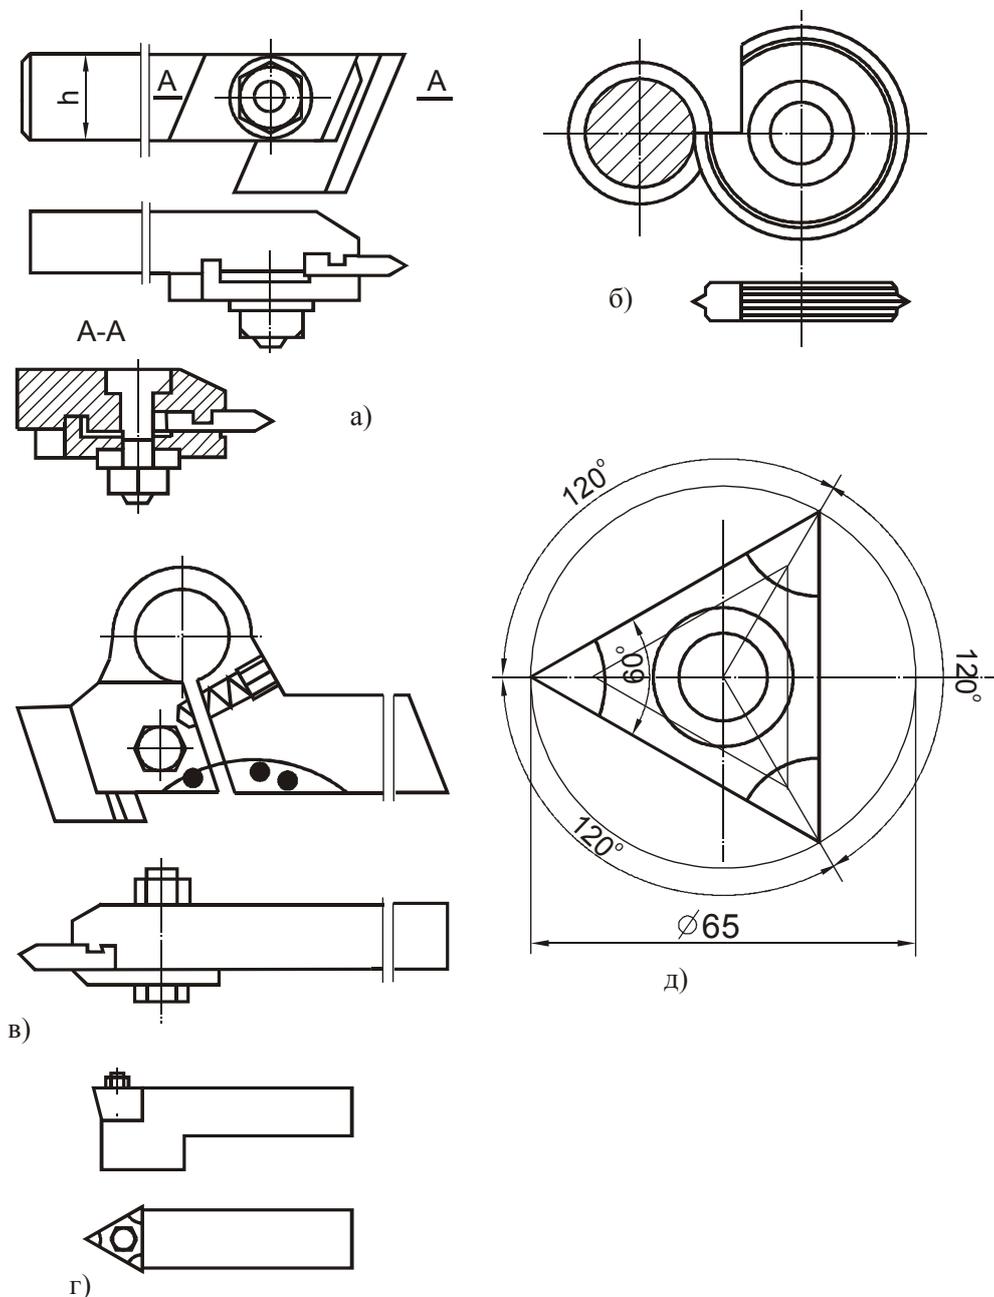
Резцы для нарезания резьбы: *a* – призматические; *б* – круглые; *в* – с пружинной державкой; *г* – с трехрезцовой головкой; *д* – трехрезцовая пластина
